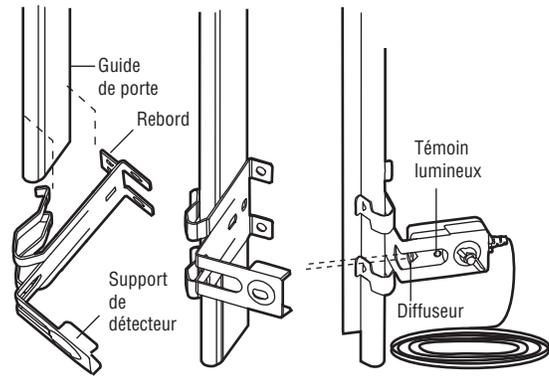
MONTAGE MURAL (CÔTÉ DROIT)
